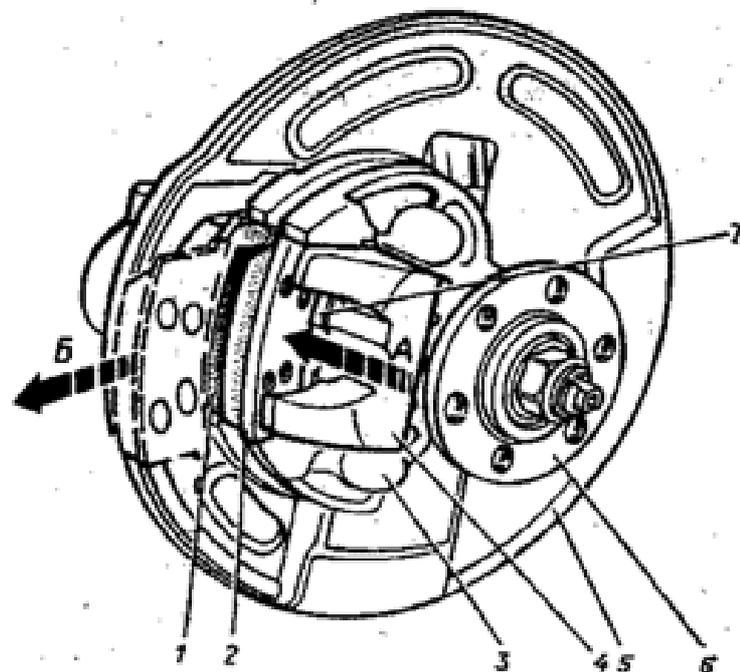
Снятие тормозных колодок переднего тормоза (диск тормоза снят): 1 - колодка внутренняя; 2 - колодка наружная; 3 - поворотный кулак; 4 - скоба тормоза; 5 - кожух грязезащитный; 6 - ступица; 7 - пружина колодок; А - колодка 2 по стрелке снята с пазов поворотного кулака; Б - колодка с небольшим поворотом снята с тормоза по стрелке
